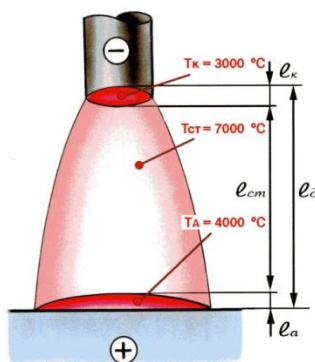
Строение и свойства сварочной дуги
